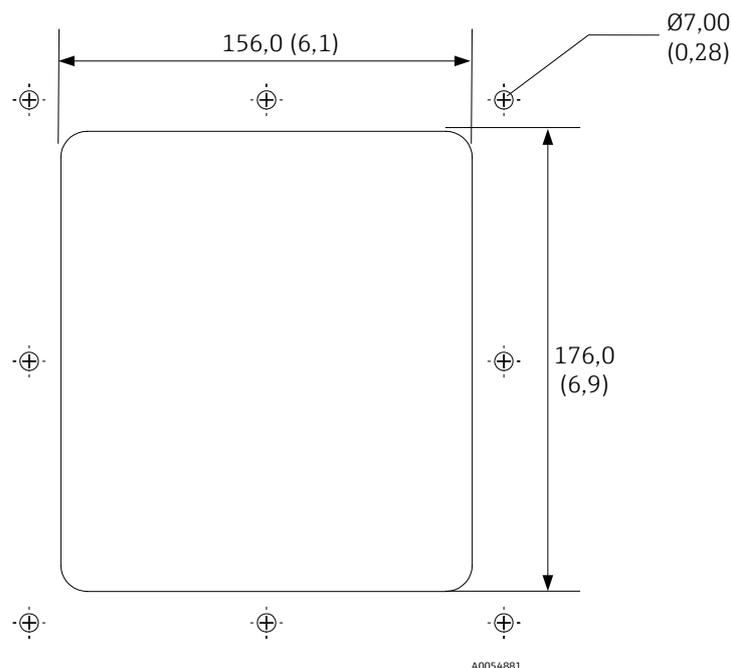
Вырез для монтажа в корпусе. Размеры: мм (дюймы)
